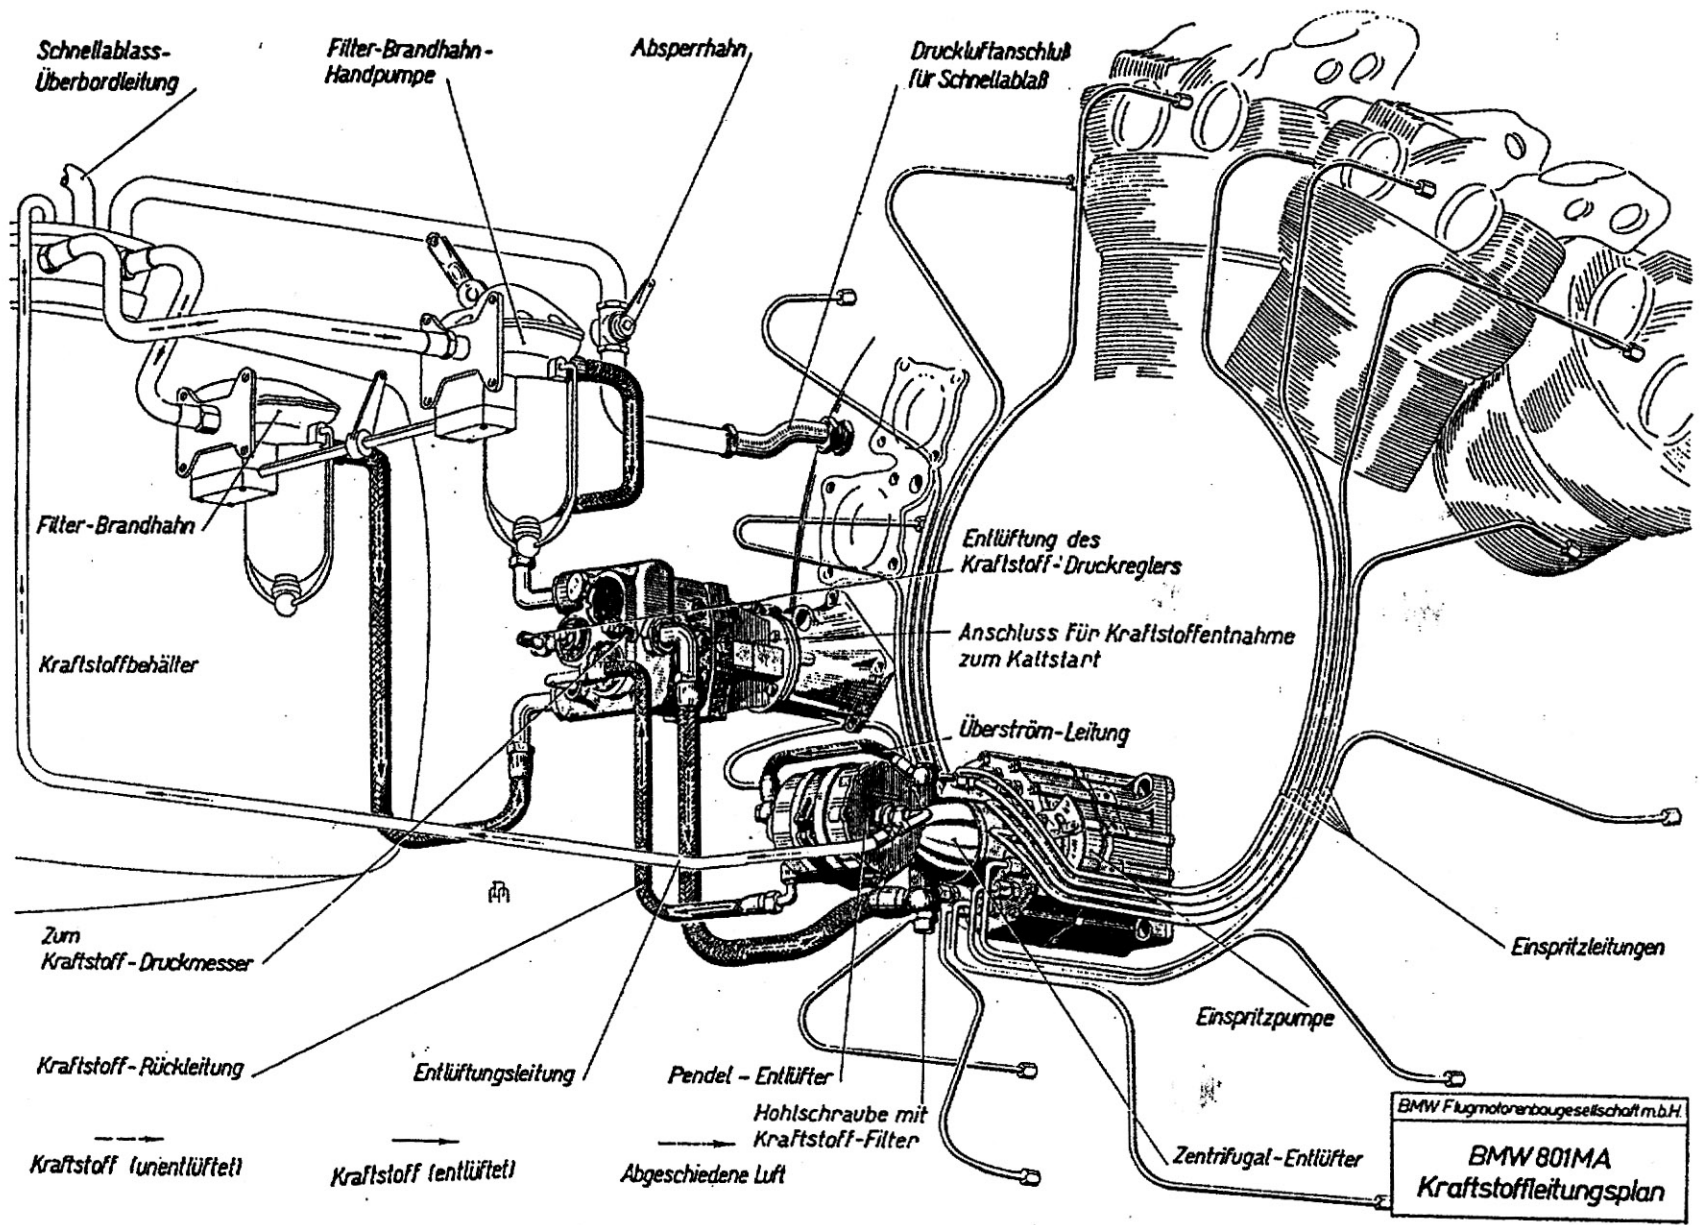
Kraftstoff-Leitungsplan BMW 801
